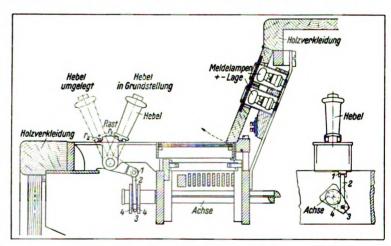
Querschnitt des Siemens-Schalterwerkes.
